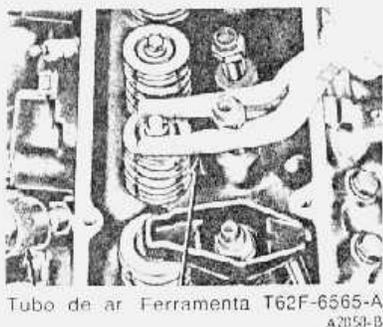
remoção ou instalação do vedador de óleo da haste da válvula
